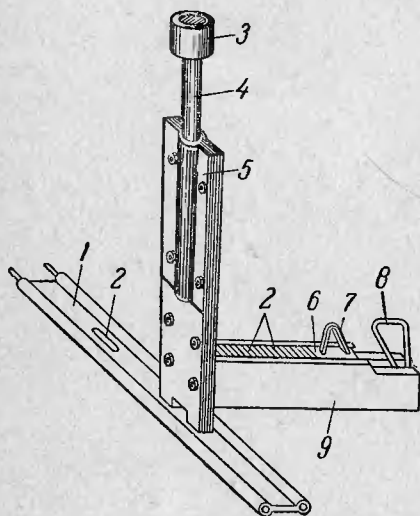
Приспособление для забивки скоб при креплении проводов ППВ или АППВ.
